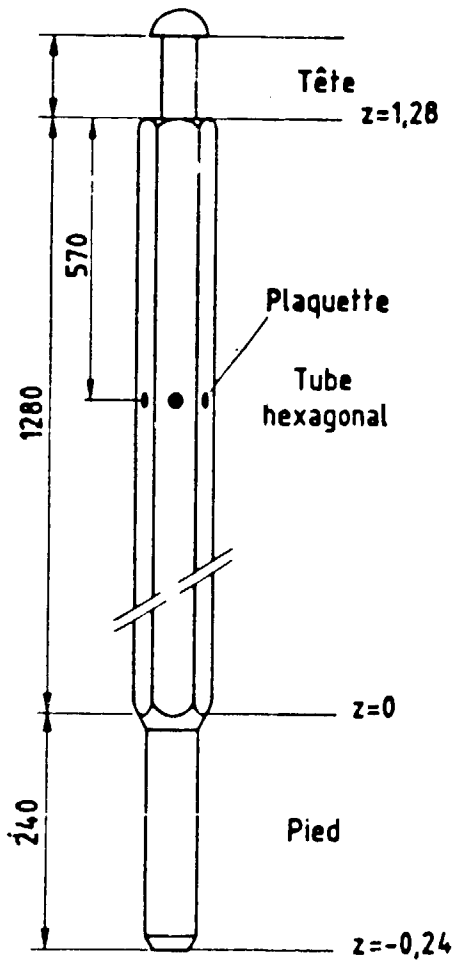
ASSEMBLAGE COMBUSTIBLE
